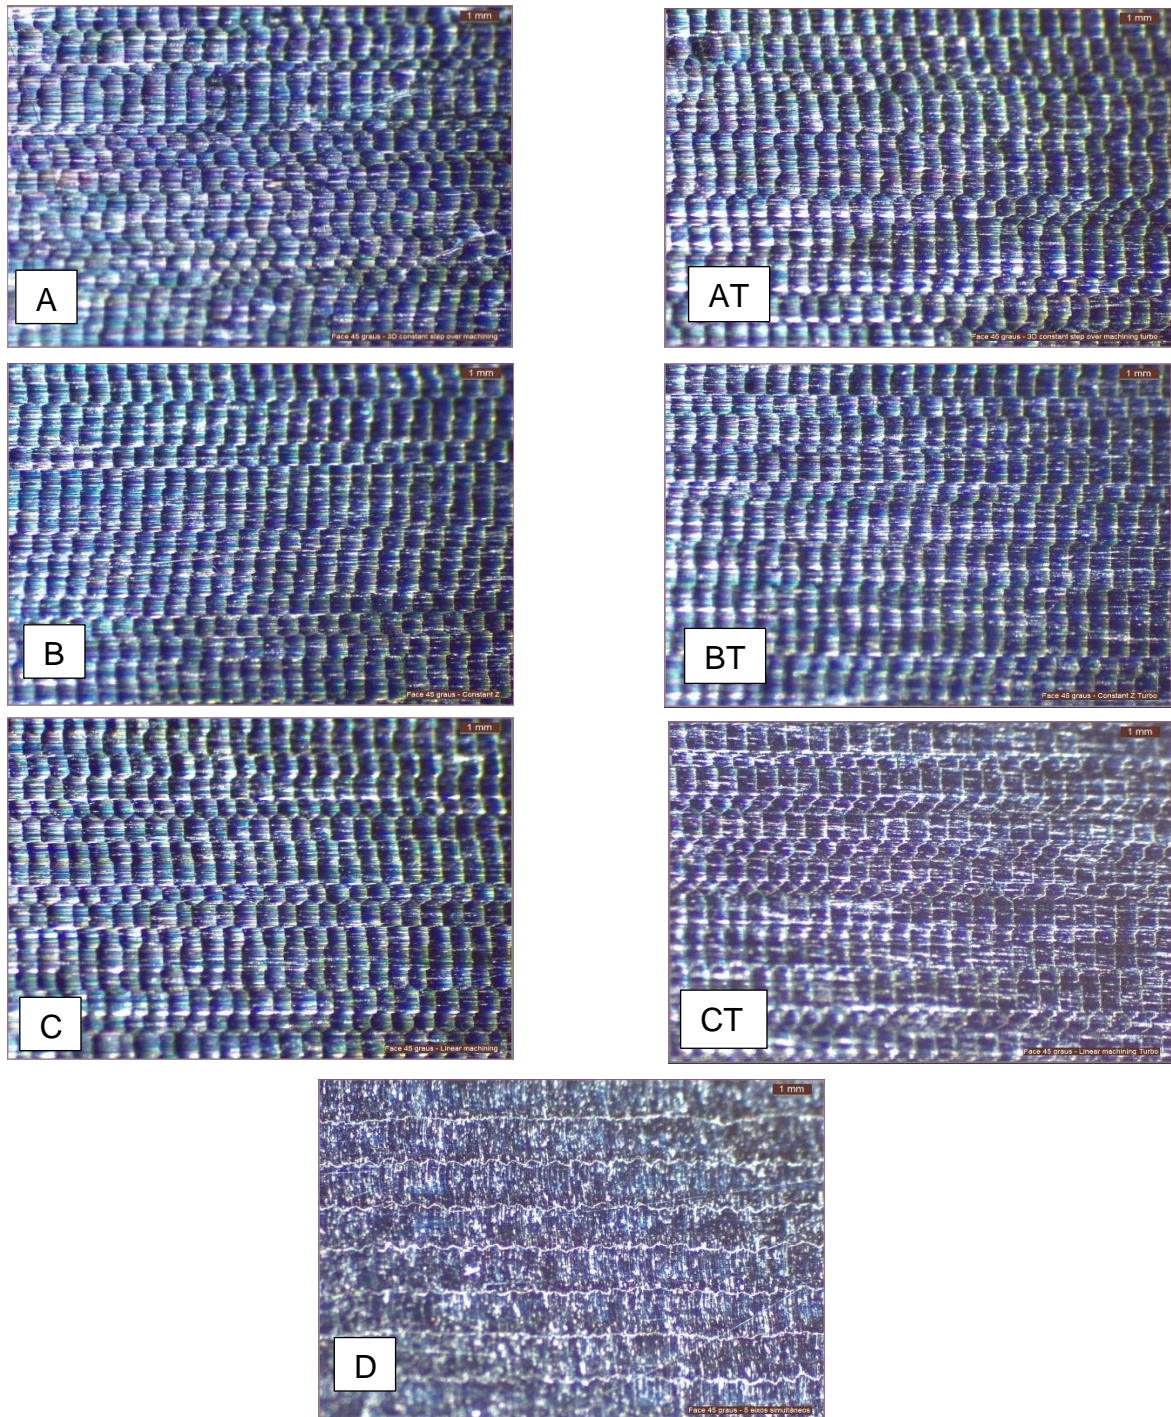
A: Estratégia de maquinagem Passagem constante 3D; AT: Estratégia de maquinagem Passagem constante 3D turbo; B: Estratégia de maquinagem Constante Z; BT: Estratégia de maquinagem Constante Z turbo; C: Estratégia de maquinagem linear; CT: Estratégia de maquinagem linear turbo; D: Estratégia de maquinagem 5 eixos simultâneos
